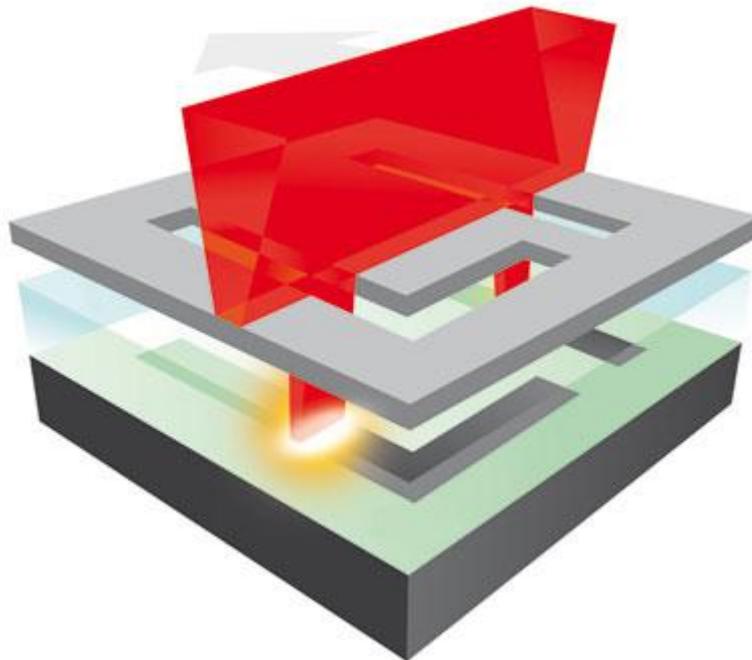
Maskenschweißen (Mask welding)
